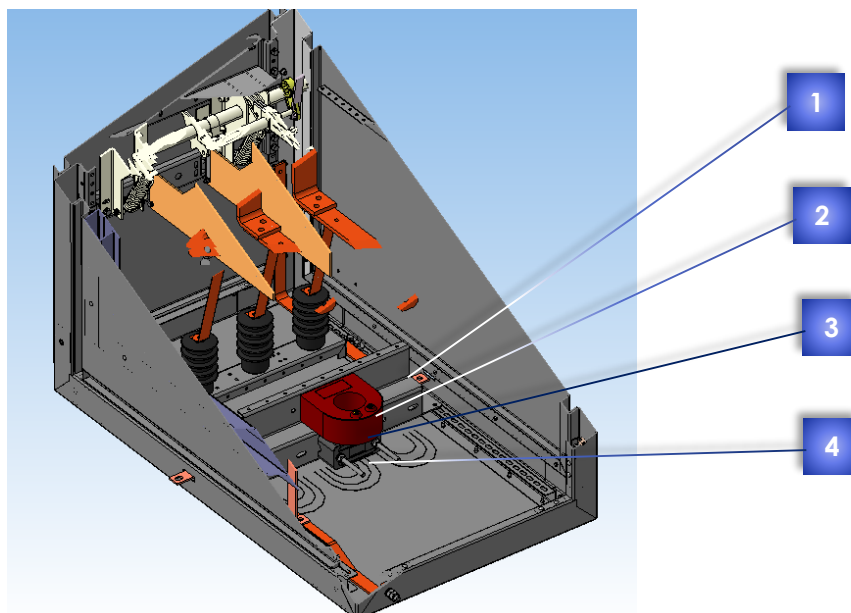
Монтаж кабеля в отсеке кабельных присоединений
